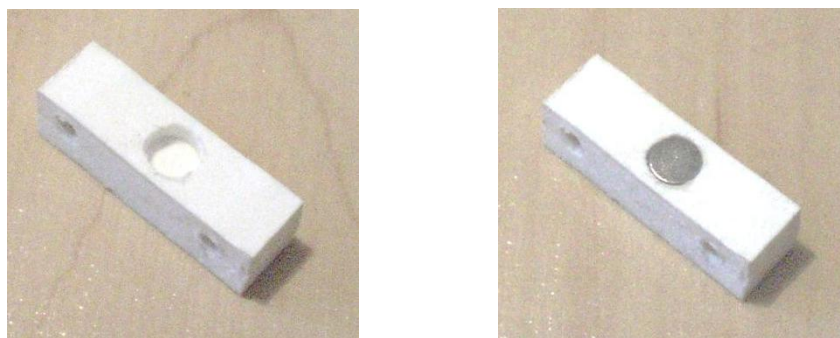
36: A la izquierda soporte para el imán con el vaciado realizado. A la derecha soporte con el imán incrustado.
